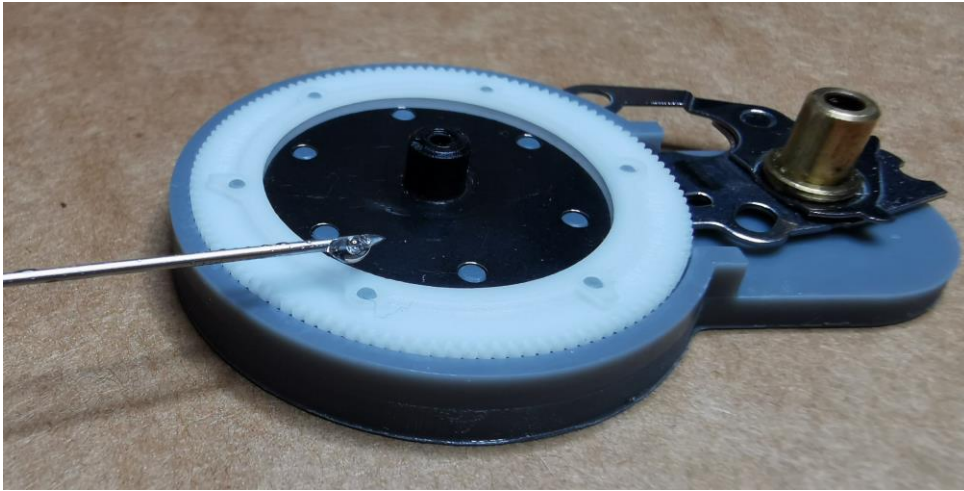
Endmontierter Zustand des CenterGear auf dem Träger
